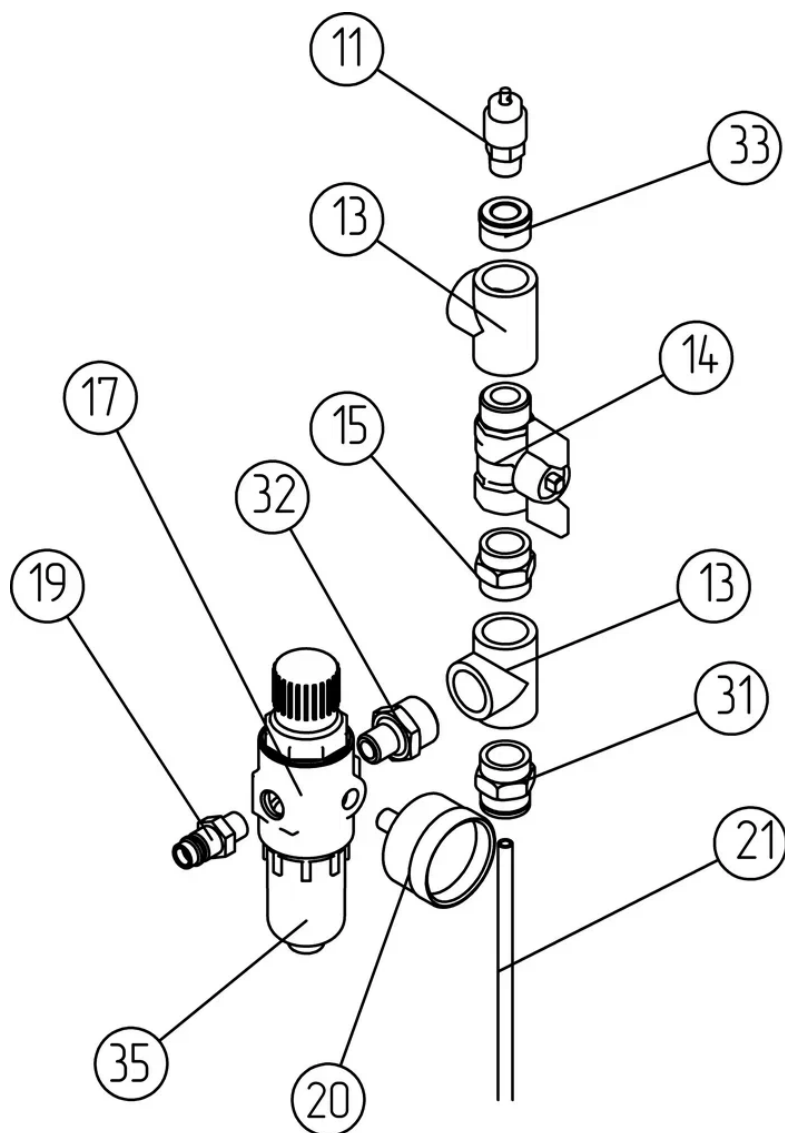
Схема сборки узла подачи воздуха (обозначения деталей согласно Рисунку 1)
